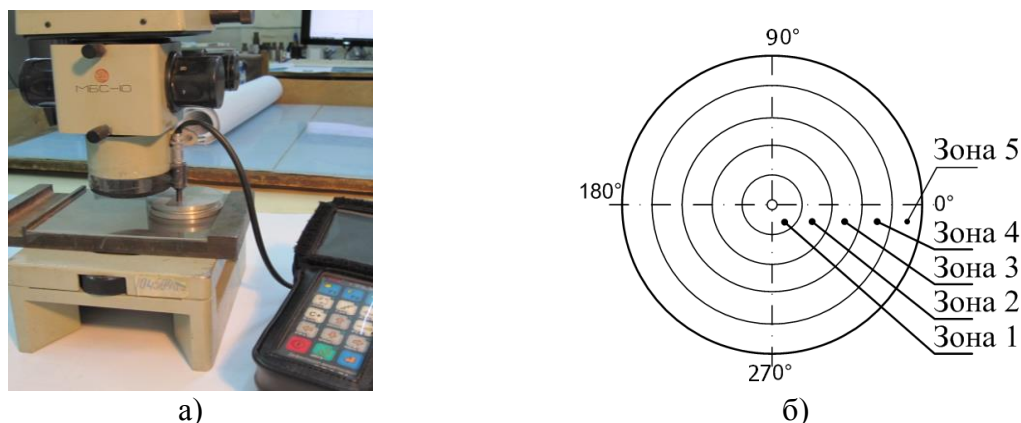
Приспособление (а) и зоны контроля алюминиевых образцов (б)
